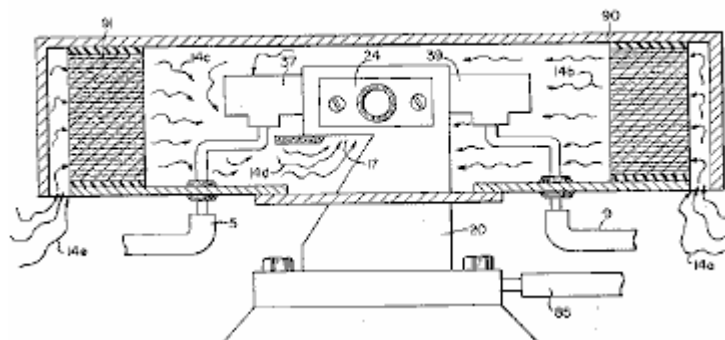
est une vue de côté de la chambre de mélange de carburant.
